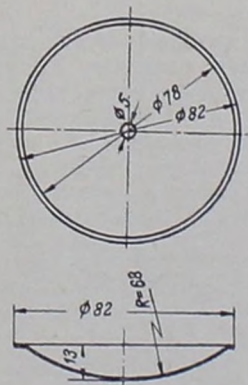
Маскировочное приспособление для стопсигнального прибора автомашины ГАЗ-АА:
